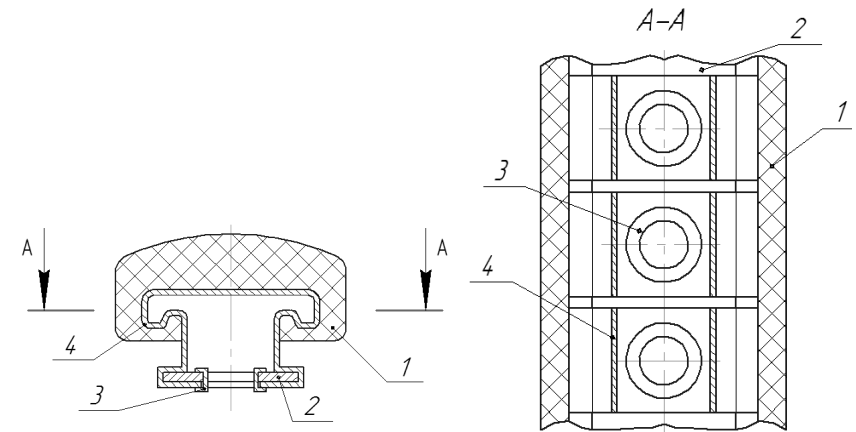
Поручень із заклепками: 1 – пружний С-подібний елемент; 2 - сталевая стрічка; 3 – заклепка; 4 – скоба-тримач
